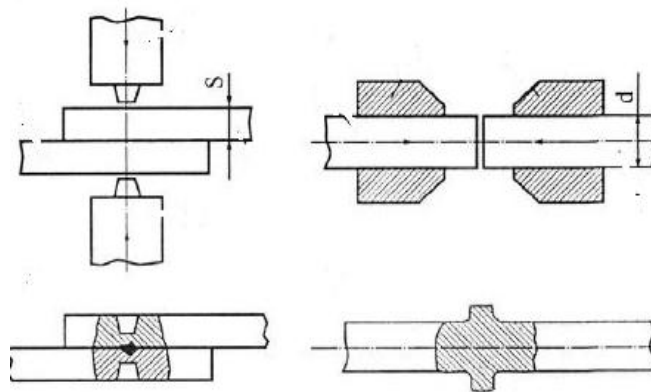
Схема холодной сварки: точечной, стыковой
